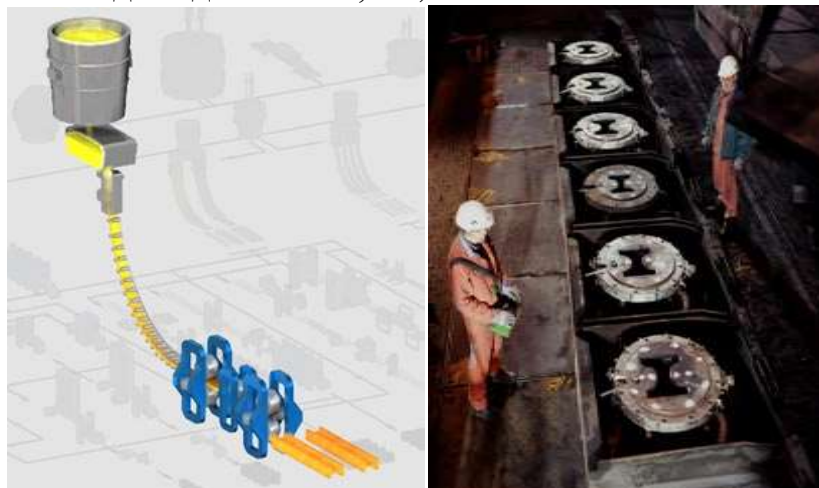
Схема МНЛЗ для разливки фасонной заготовки (слева) и расположение кристаллизаторов для разливки фасонной заготовки на 6-ти ручьевой МНЛЗ (справа)
